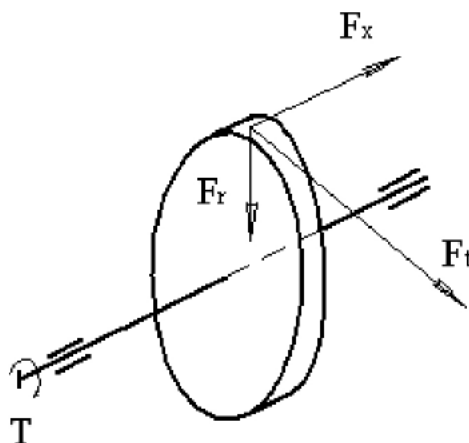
Схема сил, действующих на вал и опоры зубчатого колеса
